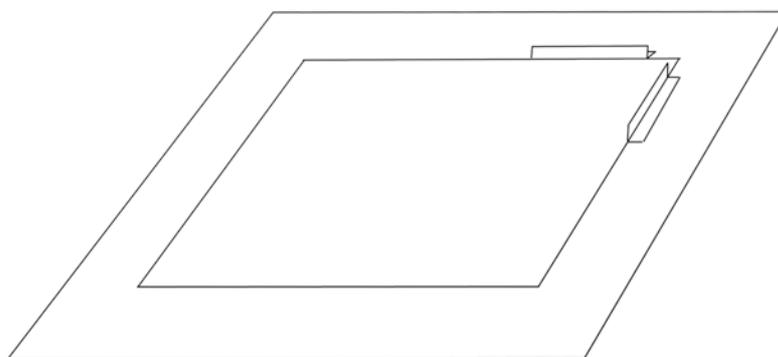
Dibujo en perspectiva de la plantilla de encaje y apantallamiento.
